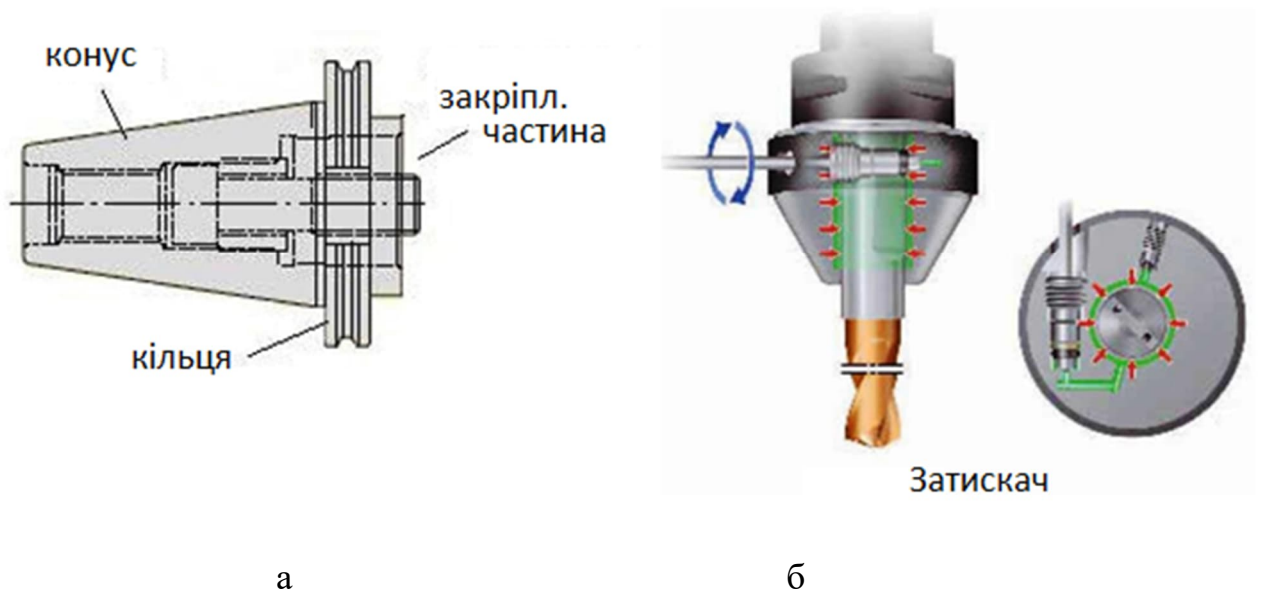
Фрезерна оправка (а) та оправка з гідропластом (б)
